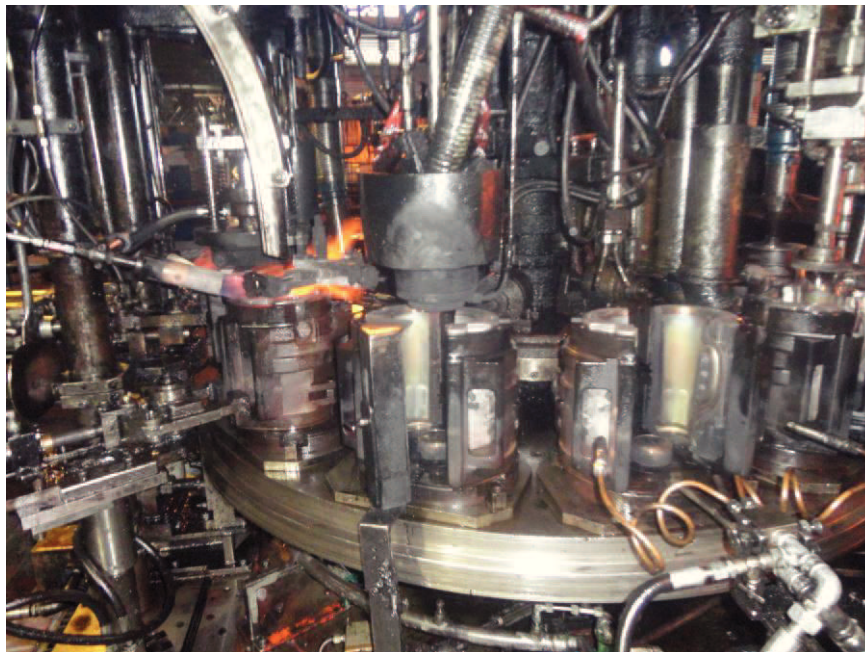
Máquina de moldação de vidro no processo prensado em moldes de abrir
